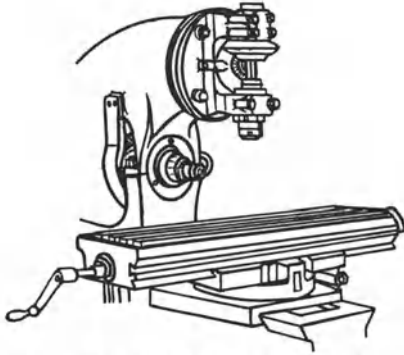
Wagrecht- und Senkrecht-Fräsmaschine von J. R. Reinecker.
